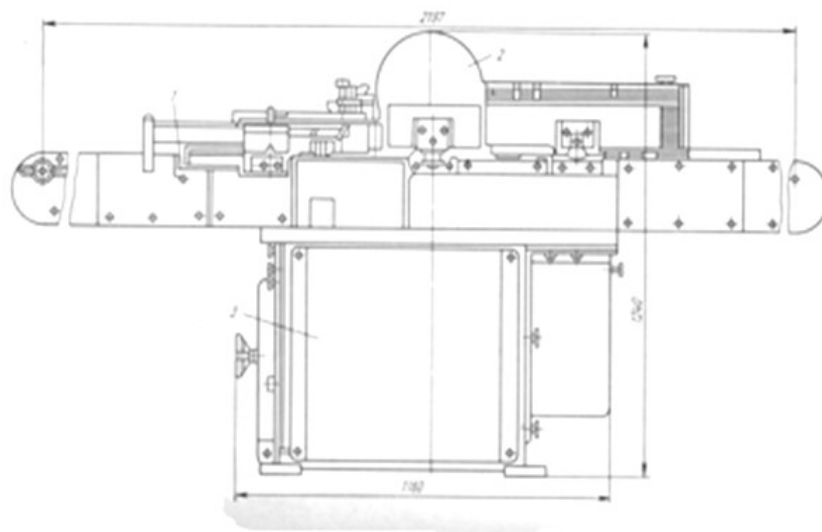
Етикетувальна машина Л5-ВЭ2-М-01: 1 — транспортер; 2 — вакуумбарабан; 3 — електрообладнання; 4 — етикетний магазин; 5 — захисне огороження; 6 — датуючий і блокувальний механізм; 7 — клеєва ванна; 8 — станина.
